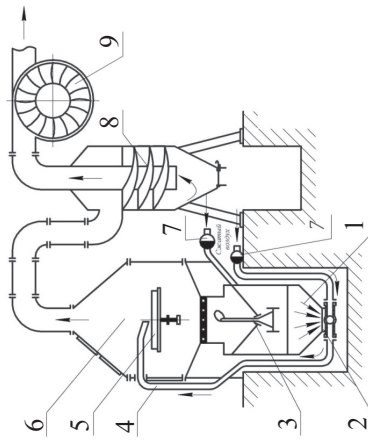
Схема процесса очистки деталей машин косточковой крошкой:
